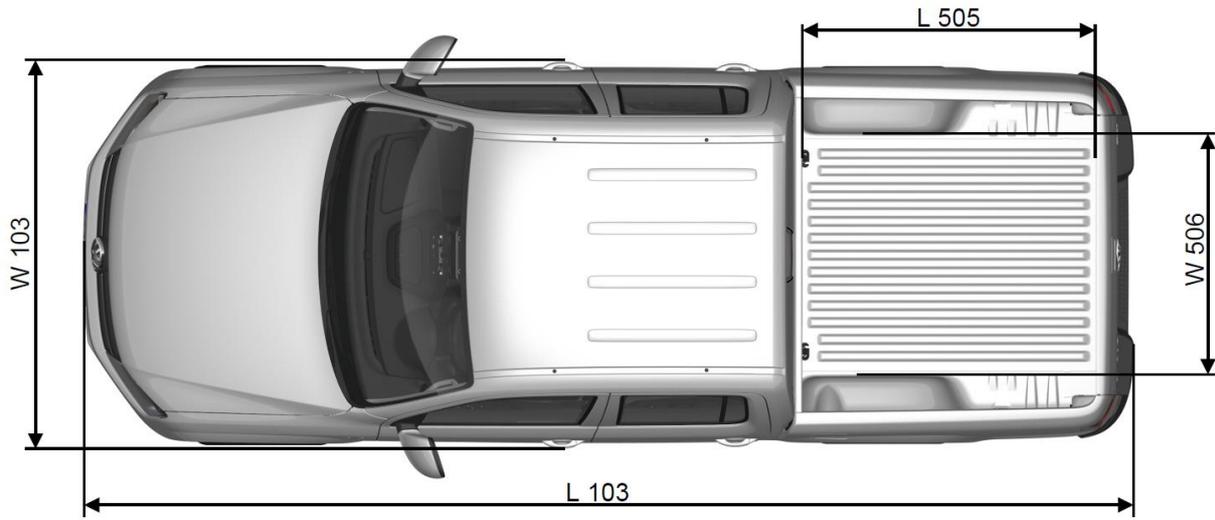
Vista de planta del Amarok DC (Double Cab)
